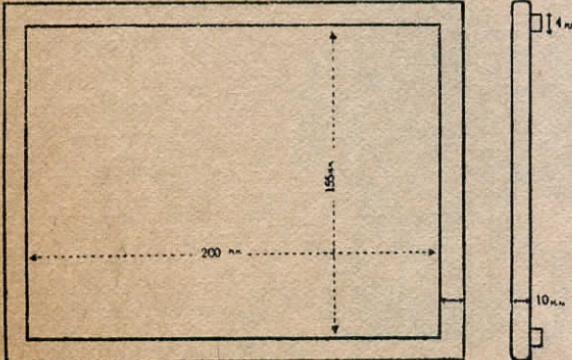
Размерный чертеж рамочки для проявления пленки.
